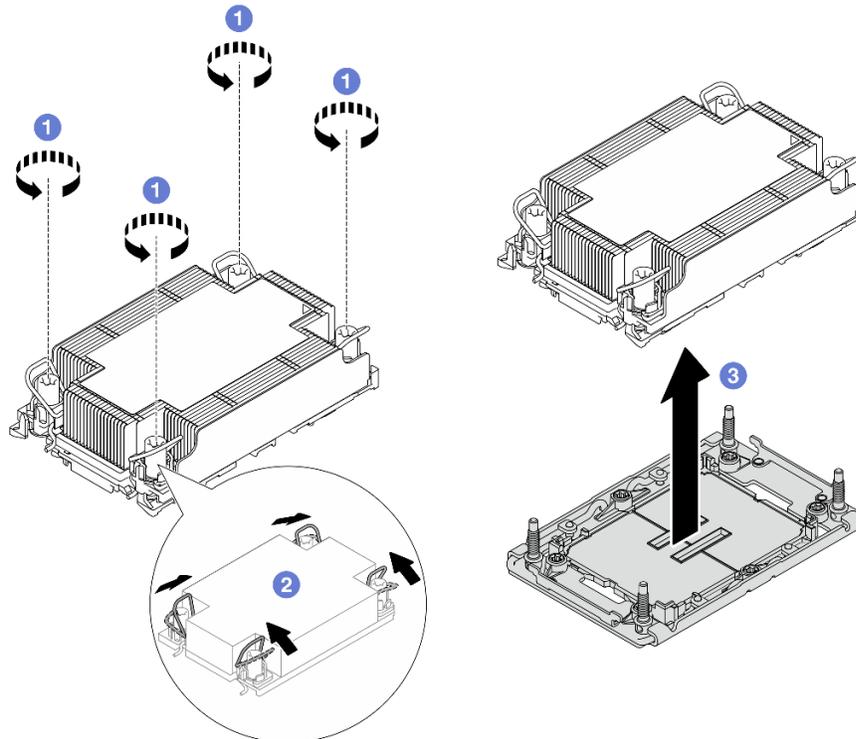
Retrait d'un module de processeur-dissipateur thermique
